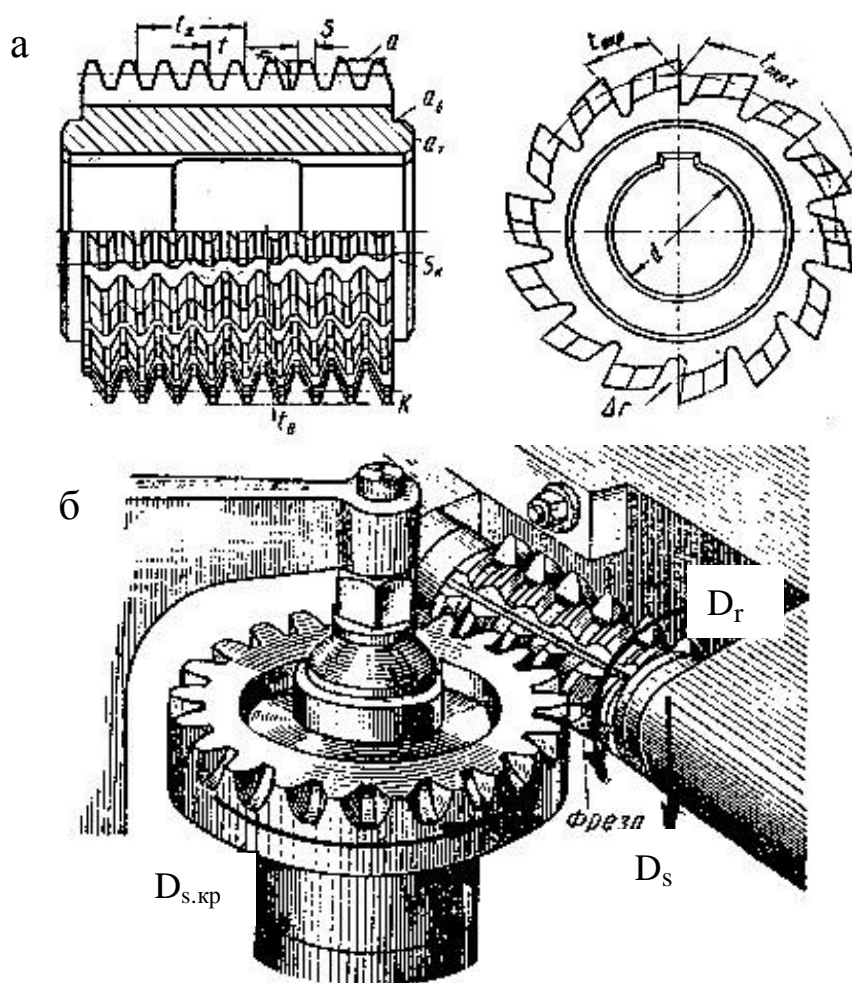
Червячная зуборезная фреза (а) и схема нарезания колеса (б)
